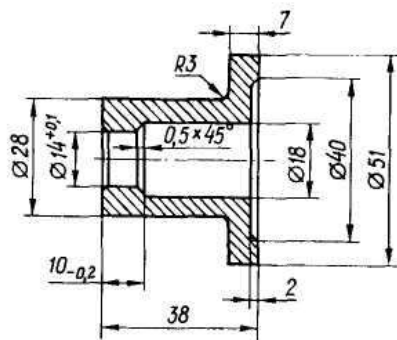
Оправка для выпрессовки и запрессовки наружного подшипника ведущего вала колёсного редуктора
